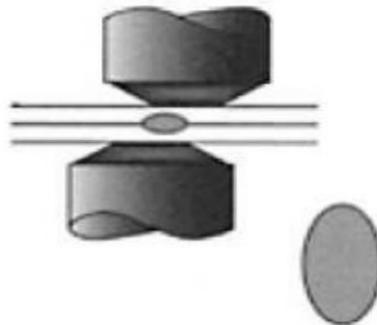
b, Punto de soldadura elíptico producido por un electrodo desalineado axialmente a una distancia.
